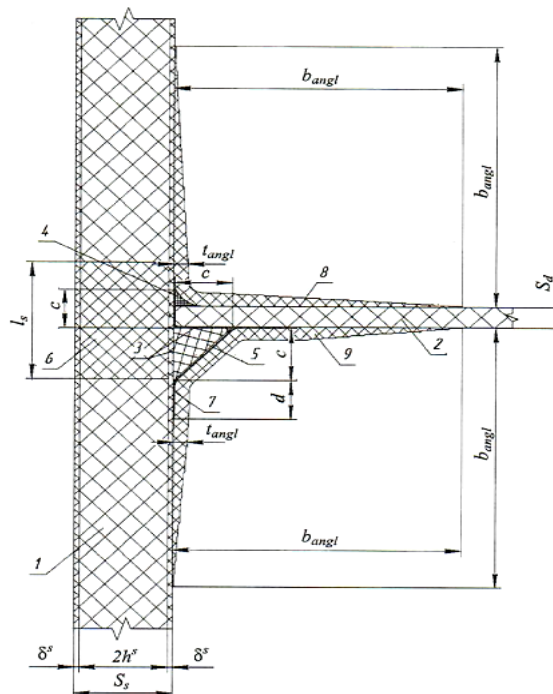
Вузол з'єднання внутрішньої палуби (платформи) одношарової конструкції з обшивкою борту тришарової конструкції:
